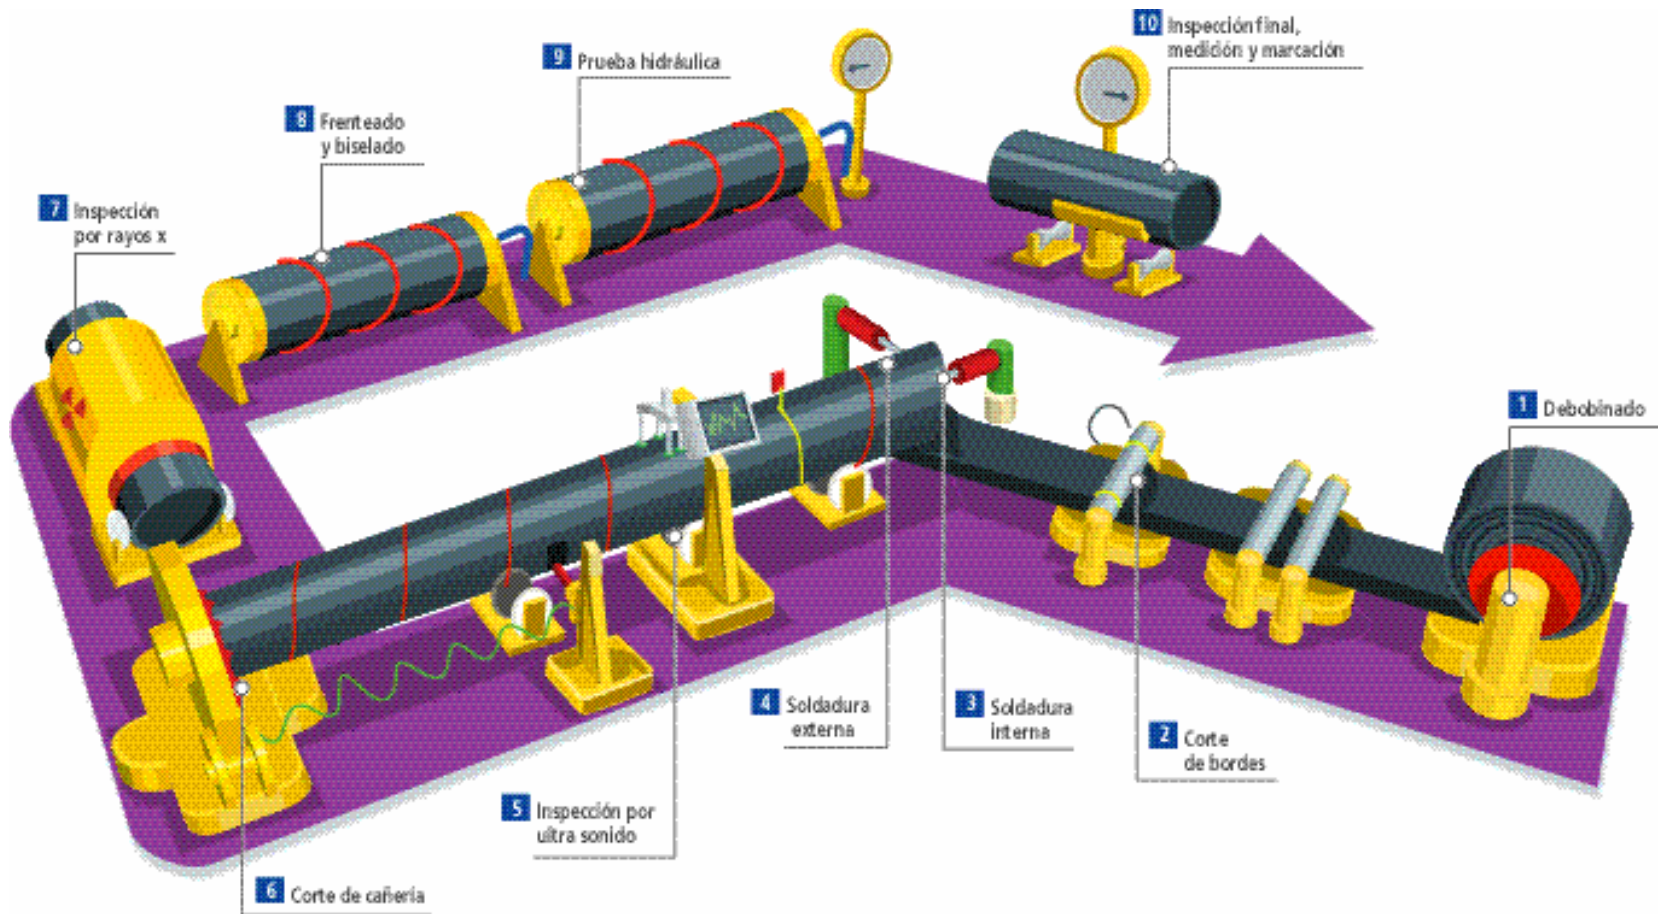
Flujo del proceso de manufactura de la tubería soldada helicoidalmente. (Figura tomada del CROWN HOLLANDER-9)
